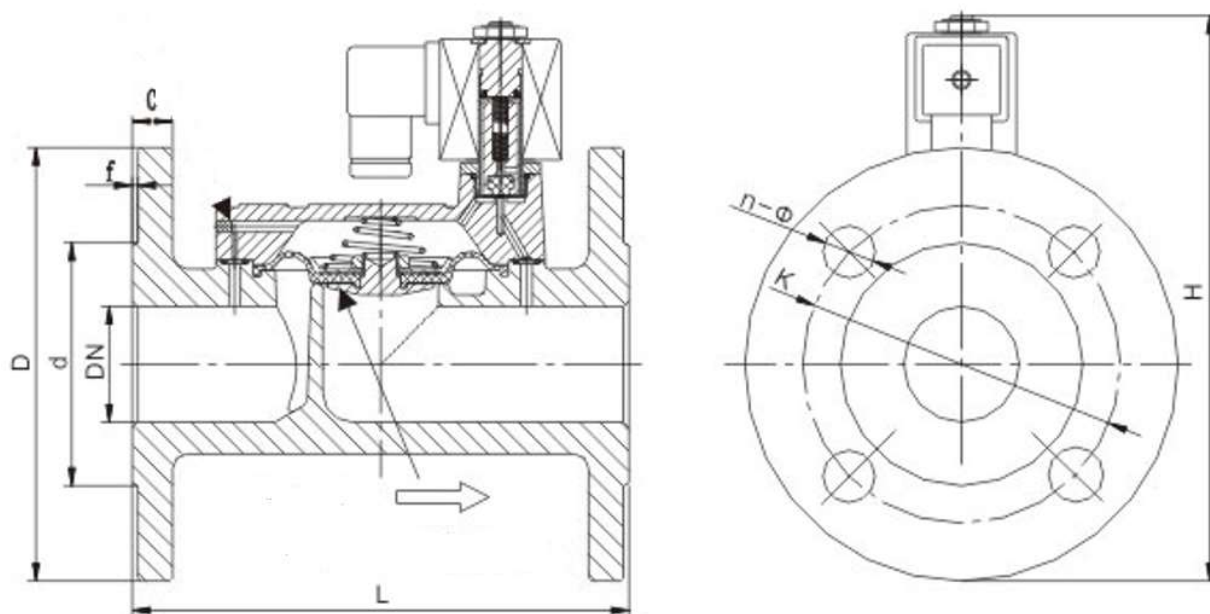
Габаритные и присоединительные размеры клапана типа EV220WR
